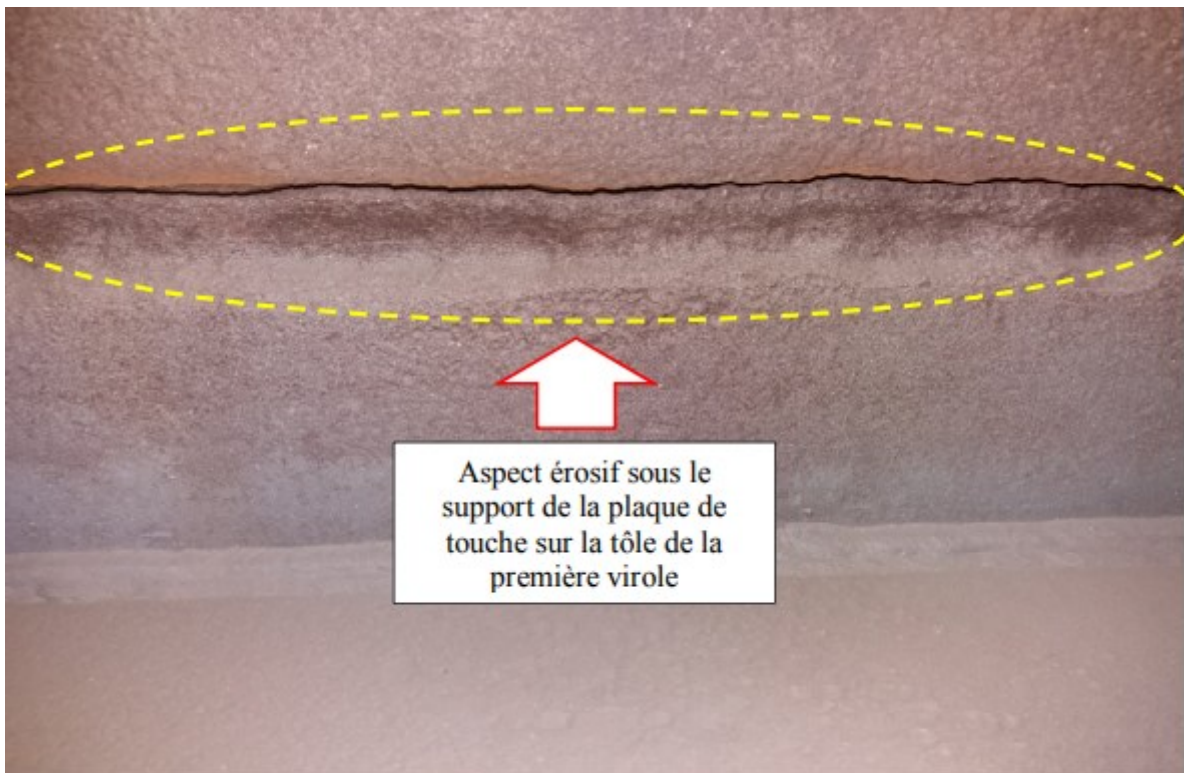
Aspect érosif sous le support de la plaque de touche sur la tôle de la première virole
